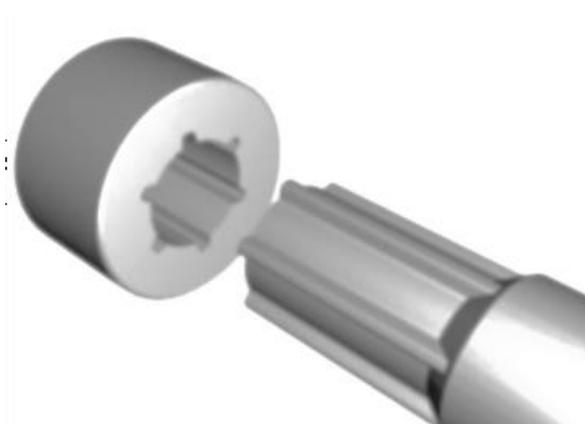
Образец зубчатого (шлицевое) соединение.
